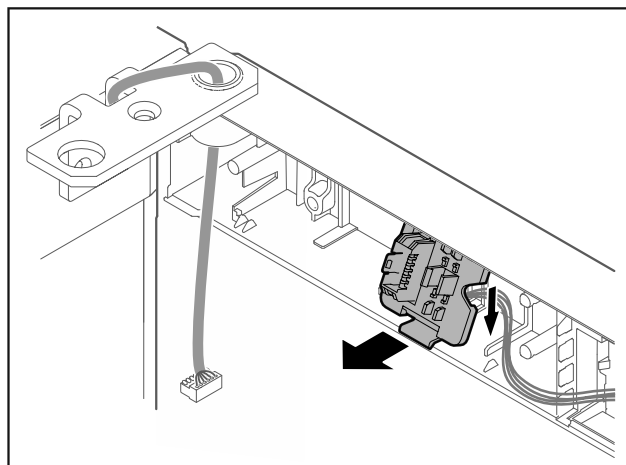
Vous pouvez tourner le support de connecteur à 180° pour le monter dans la position inverse.
